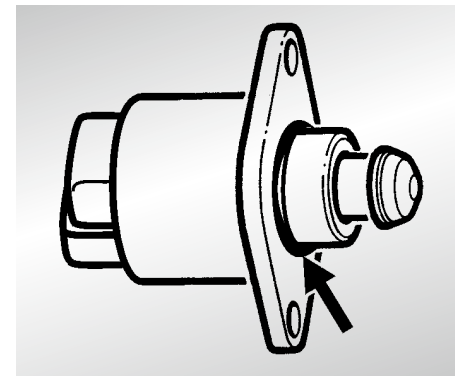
Schrittmotor mit O-Ring (Pfeil)
